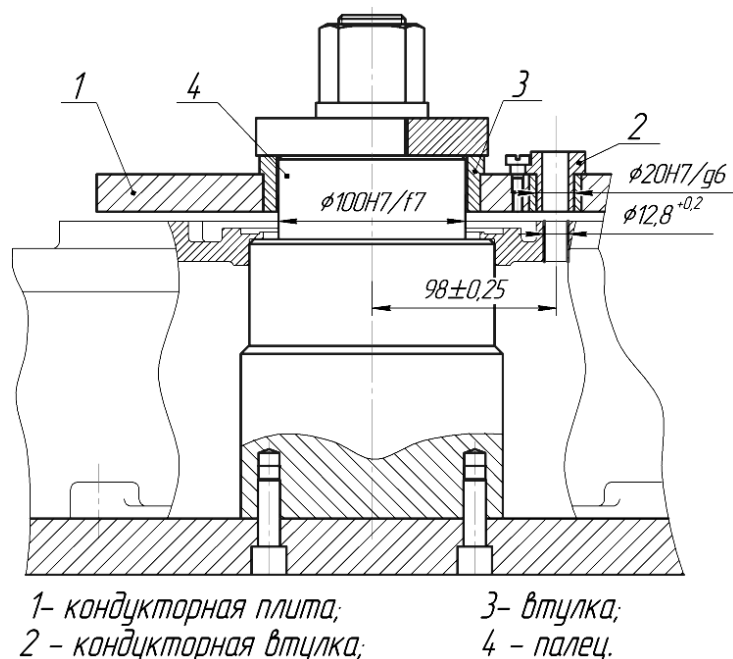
Схема базирования заготовки картера маховика в приспособлении на вертикально-сверлильной операции
